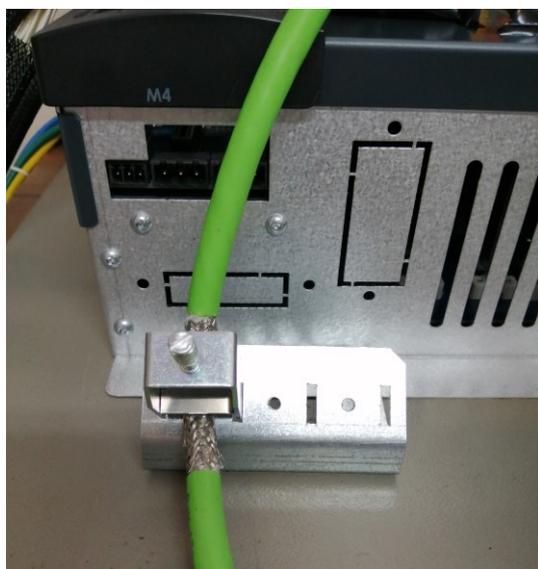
Collegamento dei cavi schermati alla staffa / Shielded cable connection to the bracket
